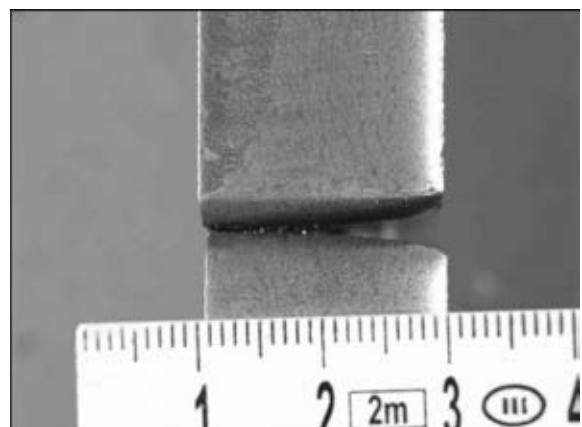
Конфигурация стыка пластин толщиной 20 мм перед сваркой
